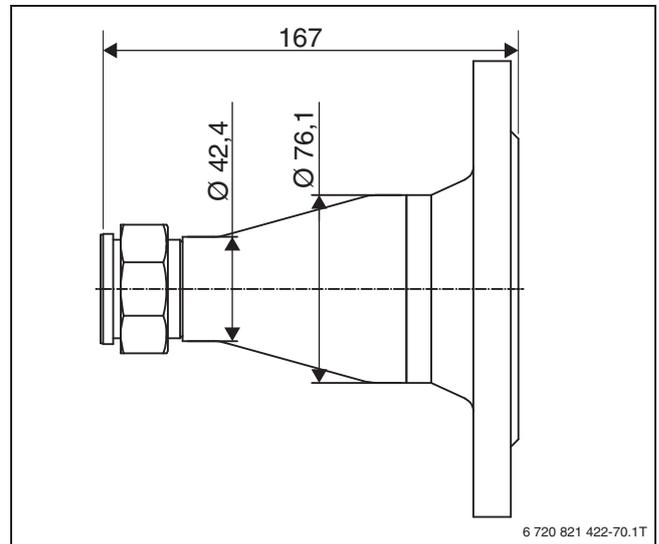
Übergangsstück DN 65/PN 16 – G 1 ½ " (Maße in mm)
